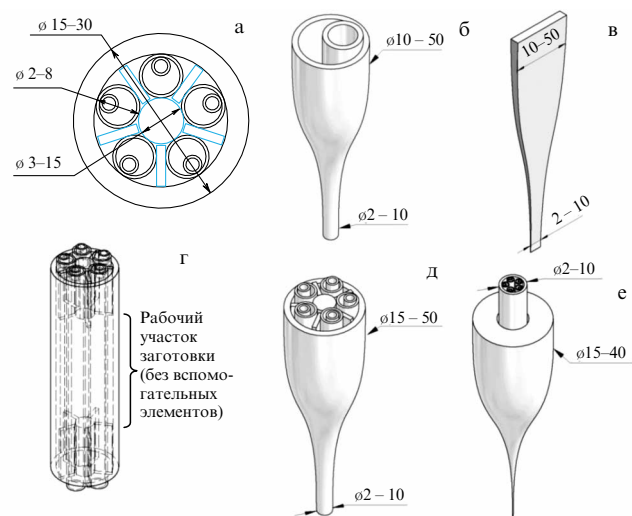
Этапы изготовления полого револьверного световода с вложенными капиллярами (приведены типичные размеры элементов в миллиметрах): (а) чертёж заготовки (голубым цветом изображены вспомогательные элементы); (б) вытяжка составных элементов с вложенными капиллярами; (в) вытяжка вспомогательных элементов; (г) собранная заготовка; (д) вытяжка промежуточной заготовки (cane); (е) вытяжка световода.
